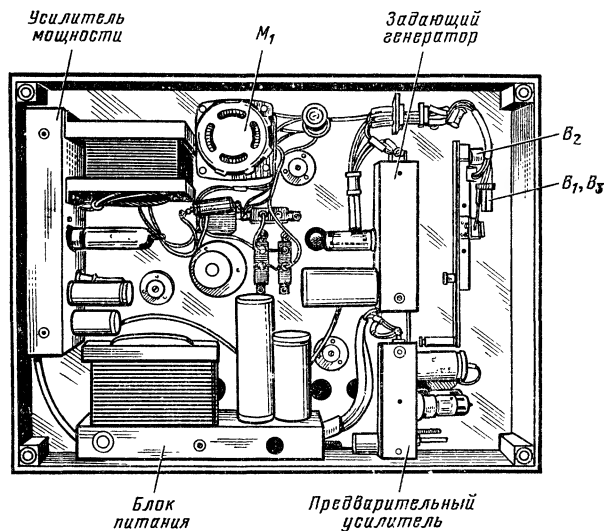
Размещение узлов проигрывателя в корпусе.
